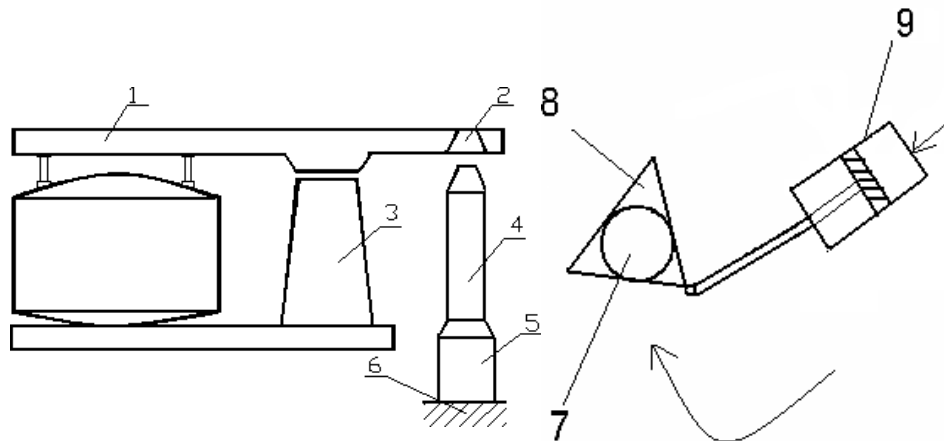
Механизм подъема и поворота свода: 1– полупортал; 2 – гнездо под опорно-поворотный вал; 3 – стойка; 4,7 – опорно-поворотный вал; 5 – гидроцилиндр; 6 – фундамент; 8 – хомут; 9 – гидроцилиндр
